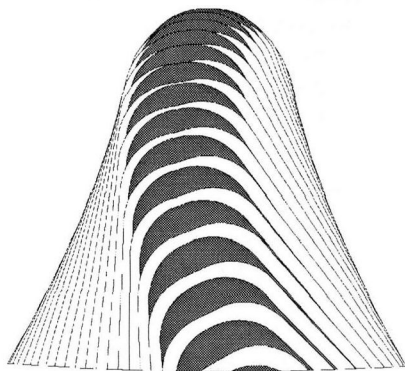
Схема формирования впадины колеса червячной фрезой с прогрессивной схемой резания. Модуль  $m = 3,5$  мм, число зубьев колеса – 36, число реек фрезы – 10
